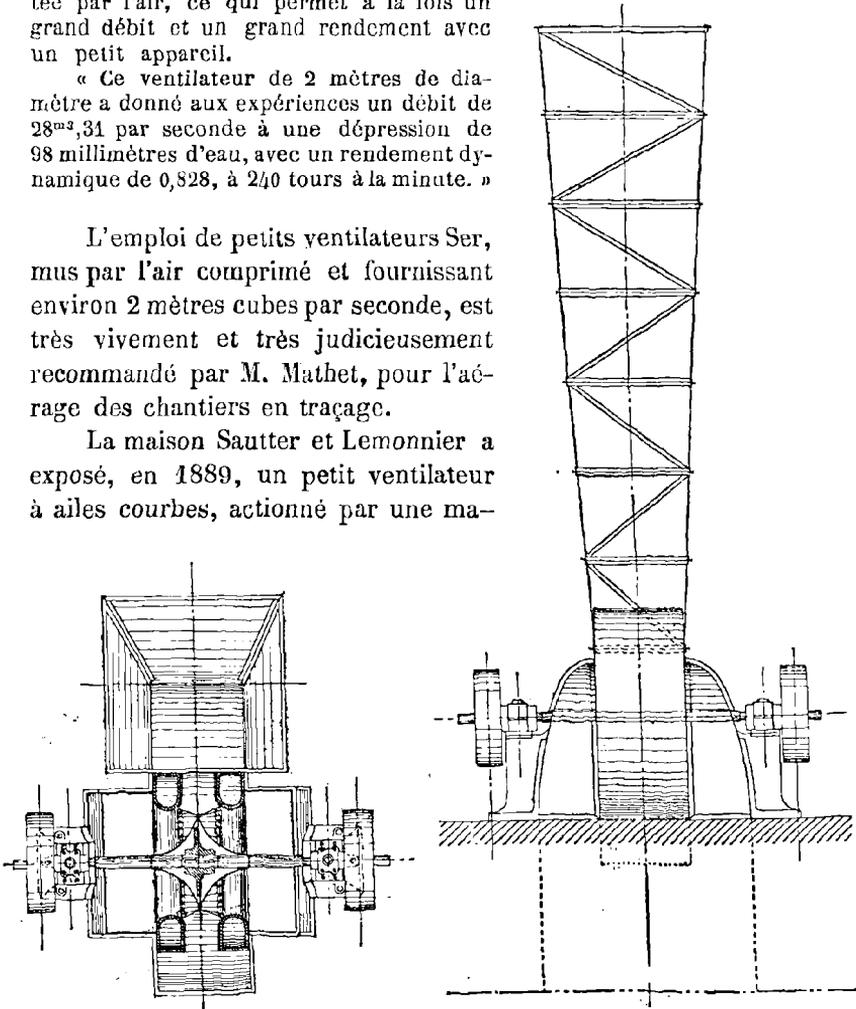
Ventilateur Ser. (Plan et élévation.)
